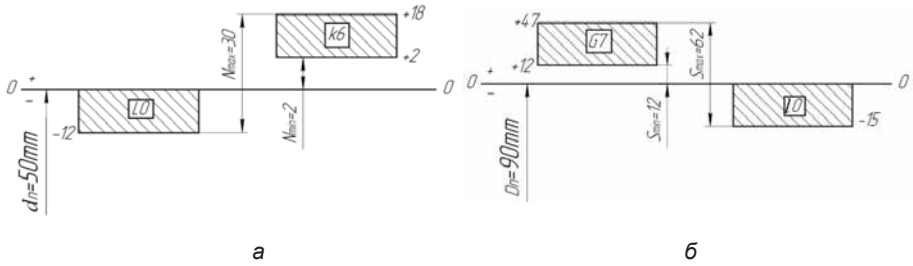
Схеми розташування полів допусків деталей з'єднання: а - „внутрішнє кільце - вал”, б - «зовнішнє кільце – корпус»
